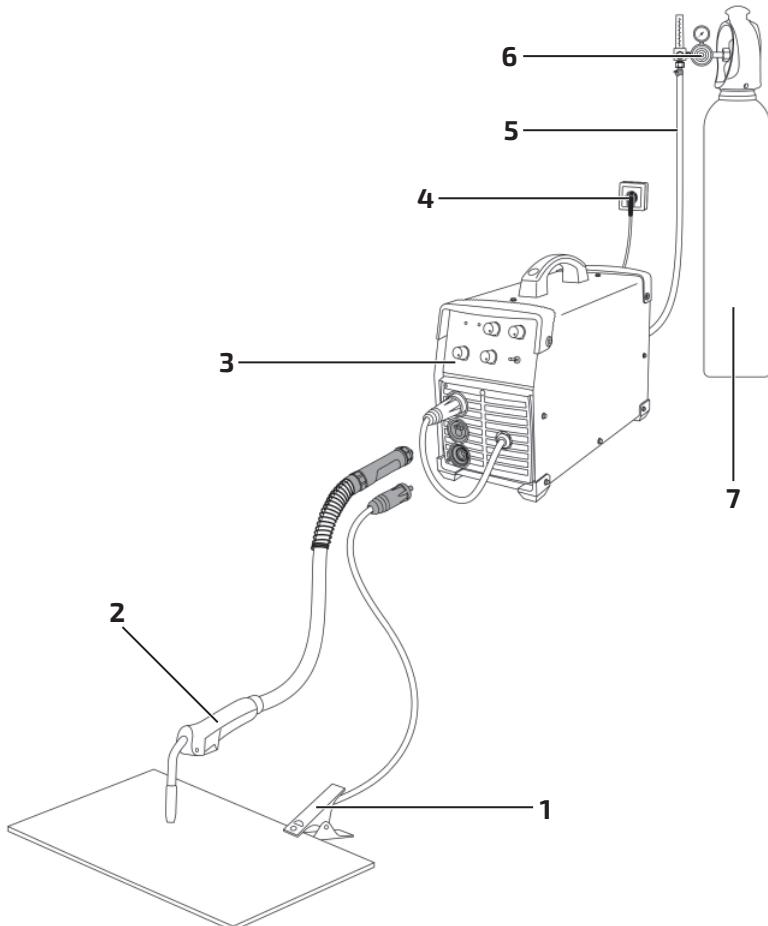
Схема подключения оборудования при сварке порошковой проволокой.
